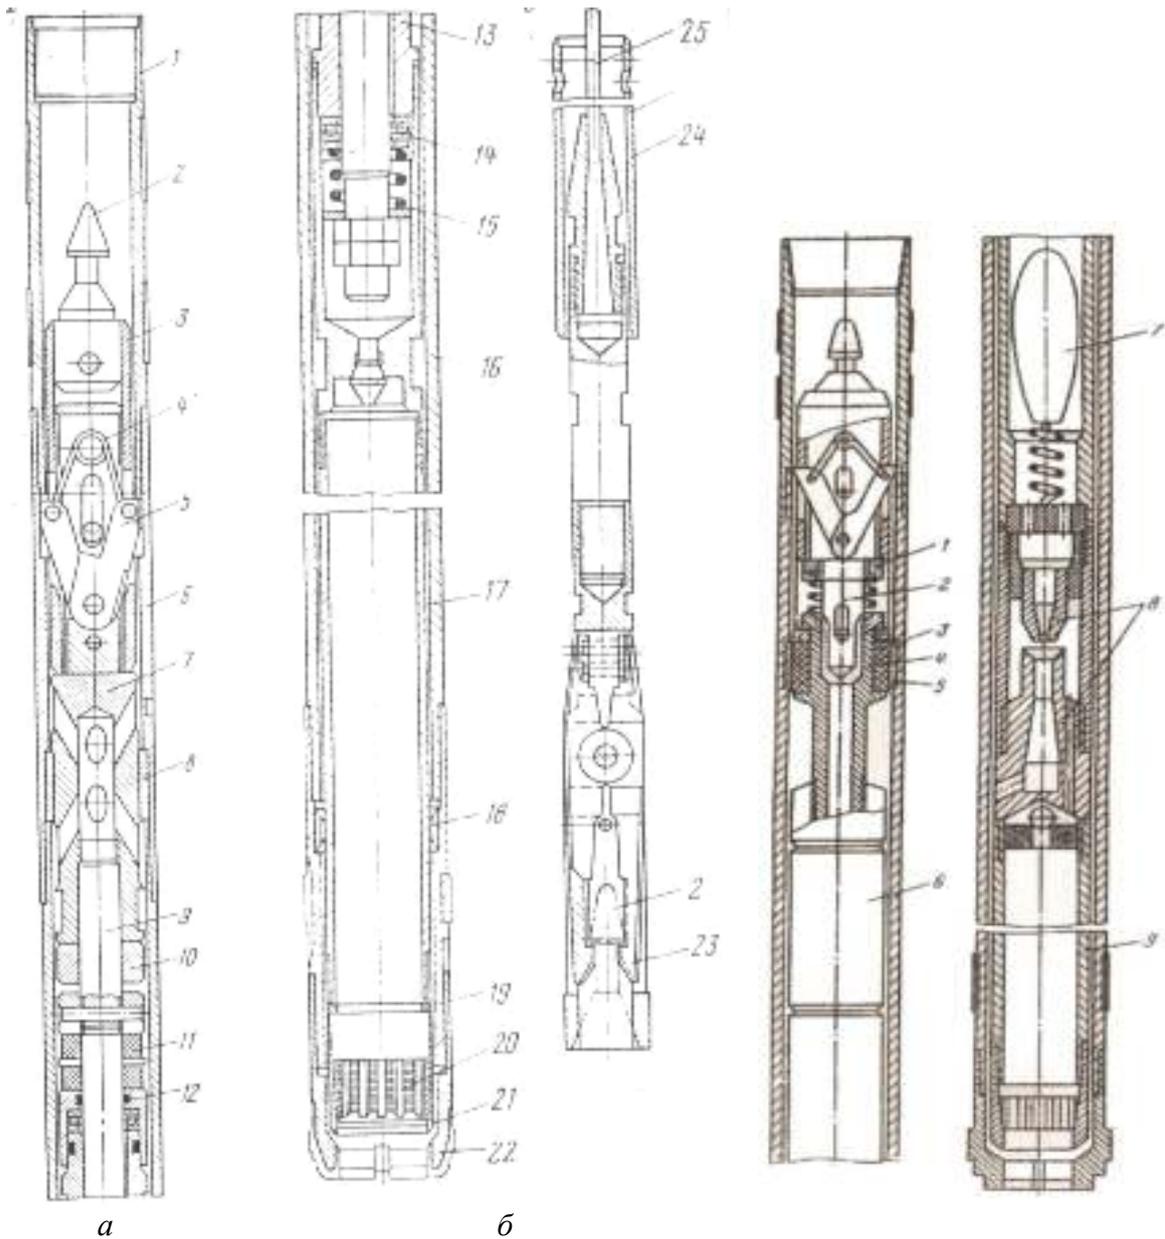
Забойный снаряд со съемной керноприемной трубой ССК: *а* – общий вид ССК конструкции ВИТР; *б* – ловитель керноприемника; 1 – релитовый переходник; 2 – головка подшипникового узла; 3 – возвратная втулка; 4 – пружина; 5 – стопоры; 6 – переходник наружной колонковой трубы; 7 – подшипниковый узел; 8 – опорное кольцо; 9 – вал; 10 – контргайка; 11 – резиновые манжеты; 12 – резиновое кольцо; 13 – направляющая втулка; 14 – упорный шарикоподшипник; 15 – пружина; 16 – наружная колонковая труба; 17 – керноприемник; 18 – стабилизатор; 19 – упорное кольцо; 20 – кернорвательное кольцо; 21 – корпус кернорвателя; 22 – алмазная коронка; 23 – захваты головки 2; 24 – патрубок, бросаемый с поверхности по канату для освобождения ловителя; 25 – стальной канат
